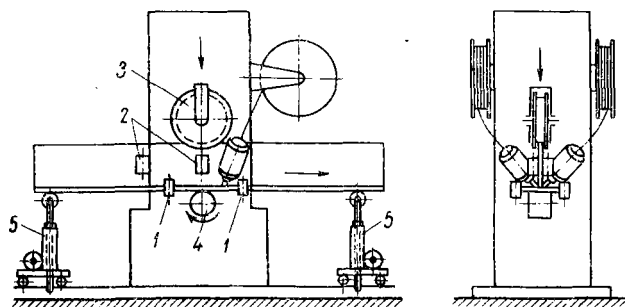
Принципиальная схема станка «СТС» для сварки балок таврового профиля
